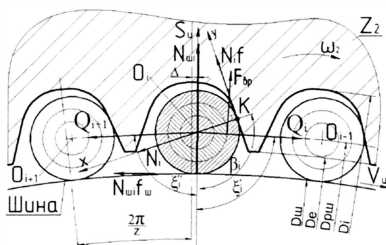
Шарниры цепи в зацеплении с ведомой звездочкой
